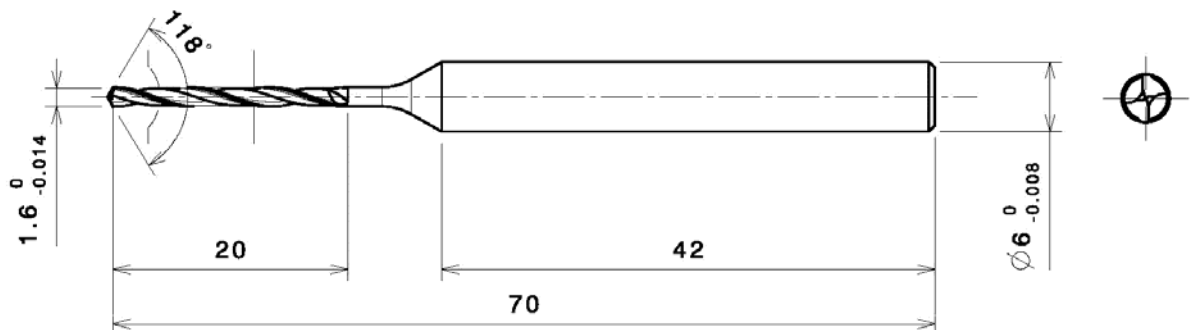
Креслення твердосплавної фрези SSD D1.6X20FX 70-6 зі сплаву UF10
